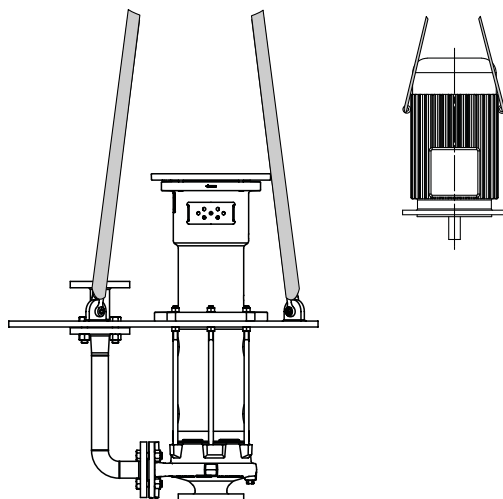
Pumpe und Motor ab Motorbaugröße 180 transportieren
